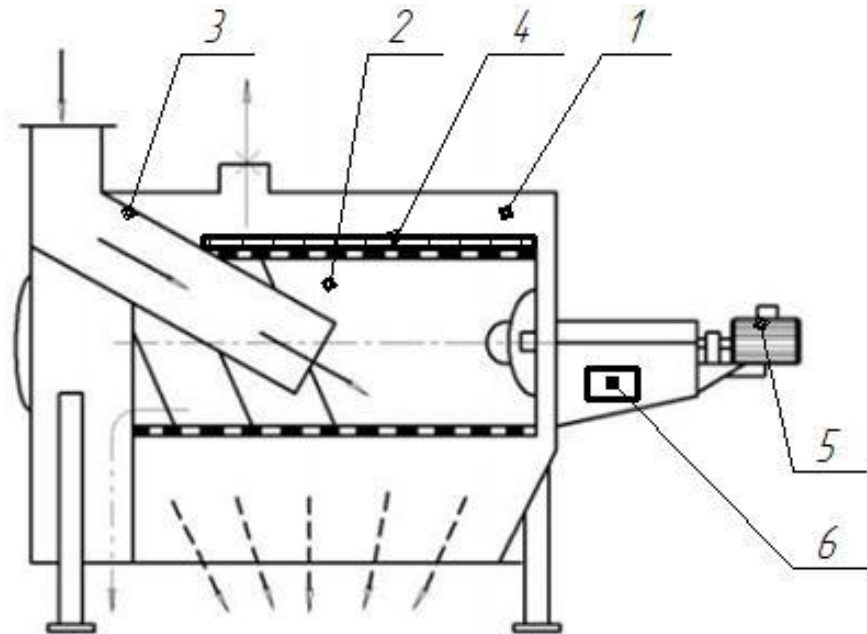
Схема зерноочисної машини скальператорного типу А1-БЗО
